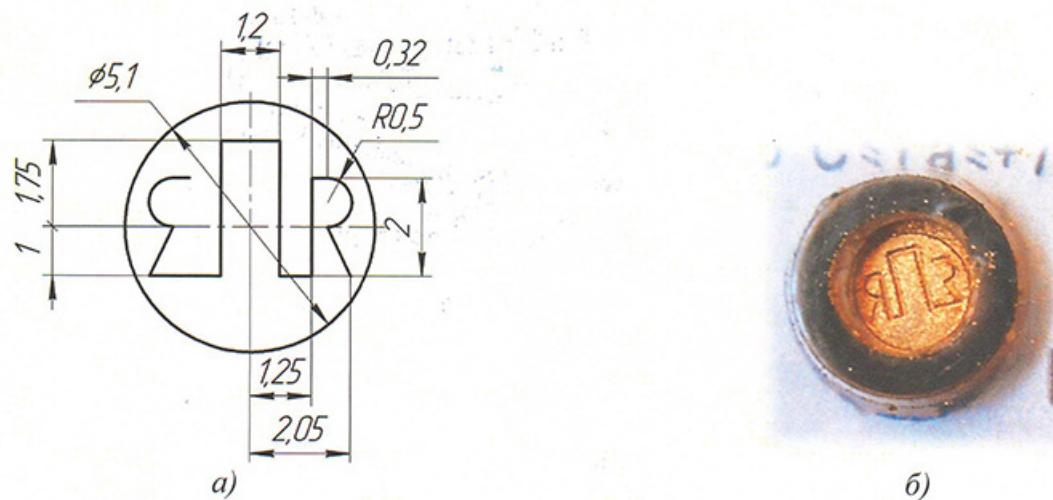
Геометричні параметри (а) та загальний вигляд (б) відбитку тавра виробника, що застосовується для пломбування гвинта, встановленого в корпусі лічильника
